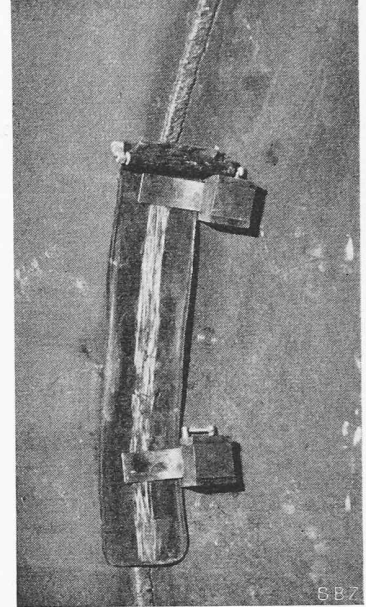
Schweissnahtprüfung im Druckschacht. Auf der Innenseite des Panzerrohres wird ein Filmstreifen auf die Schweissnaht geklemmt
